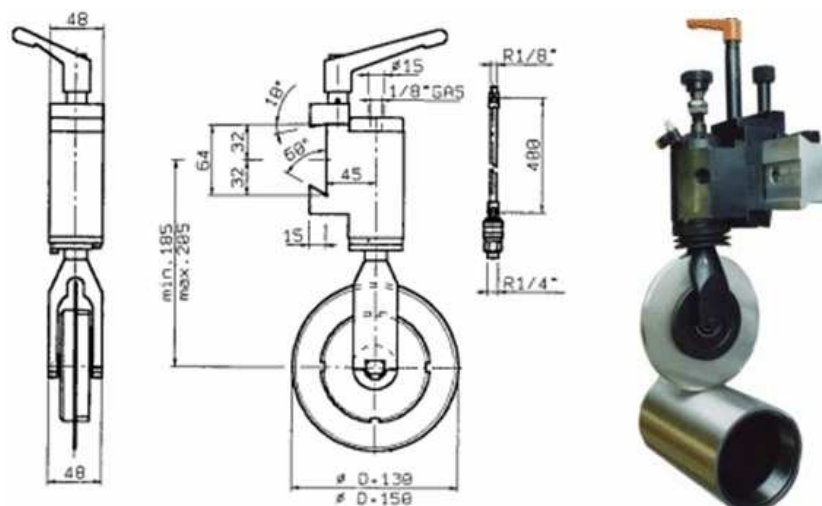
Cuchilla circular de corte a presión<sup>10</sup>.
